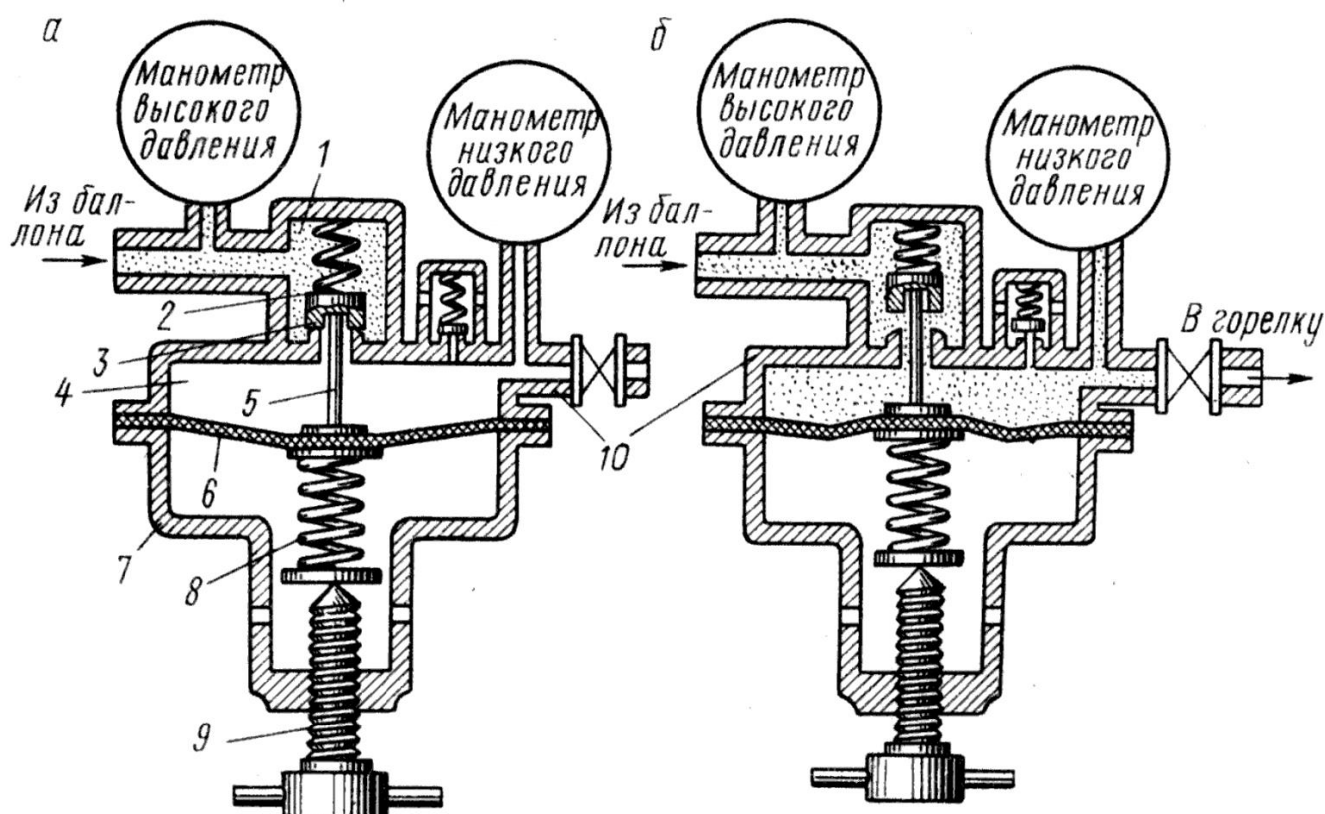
Схема однокамерного газового редуктора: а – нерабочее положение; б – рабочее положение; 1 – камера высокого давления; 2 – клапан; 3 – седло; 4 – камера низкого давления; 5 – шток; 6 – мембрана; 7 – крышка; 8 – пружина; 9 – винт регулировочный; 10 – корпус
